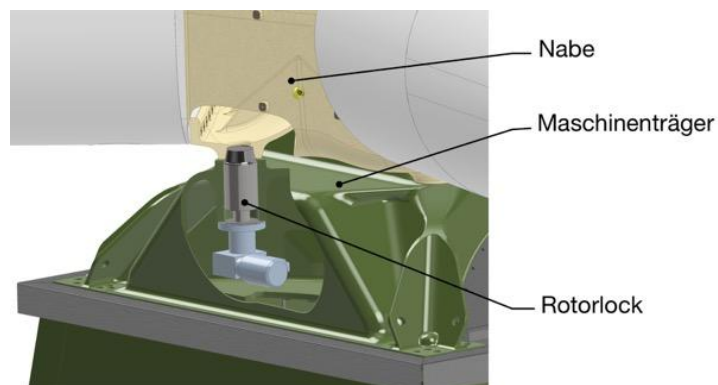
Manuelle Rotorblockierung durch Rotorlock
